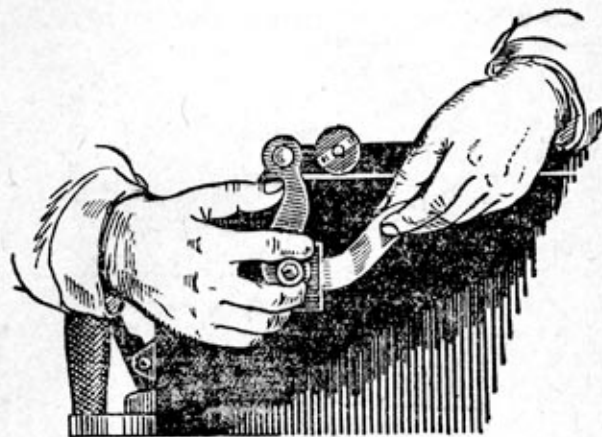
Проверка зазора между выступом рамы и стенкой корпуса
